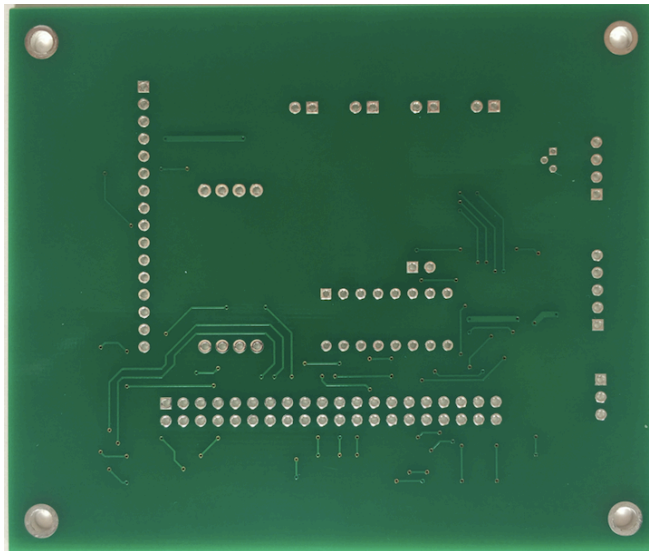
Imagen de capa *bottom* de la PCB real una vez fabricada.
